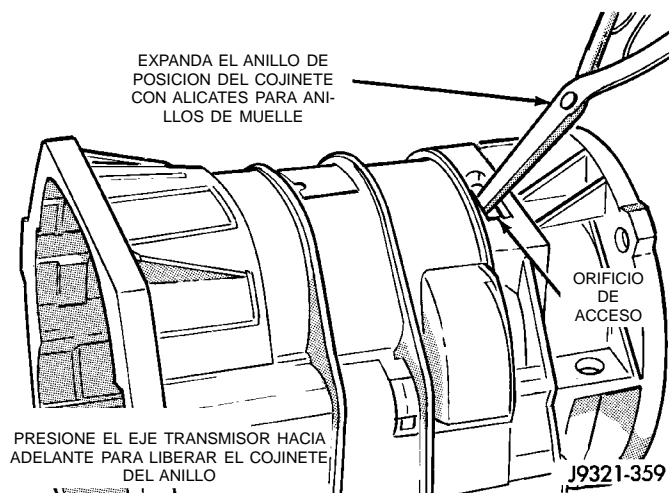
Asiento del anillo de posición en el cojinete trasero
